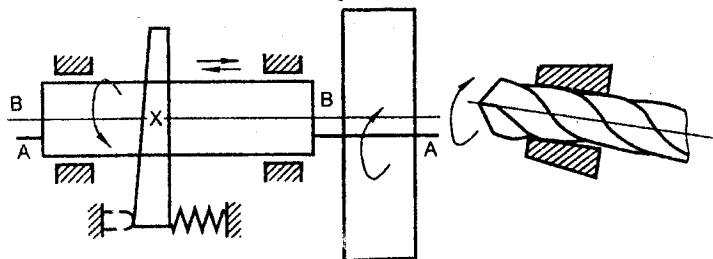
Схема заточування свердла по гвинтовій поверхні
